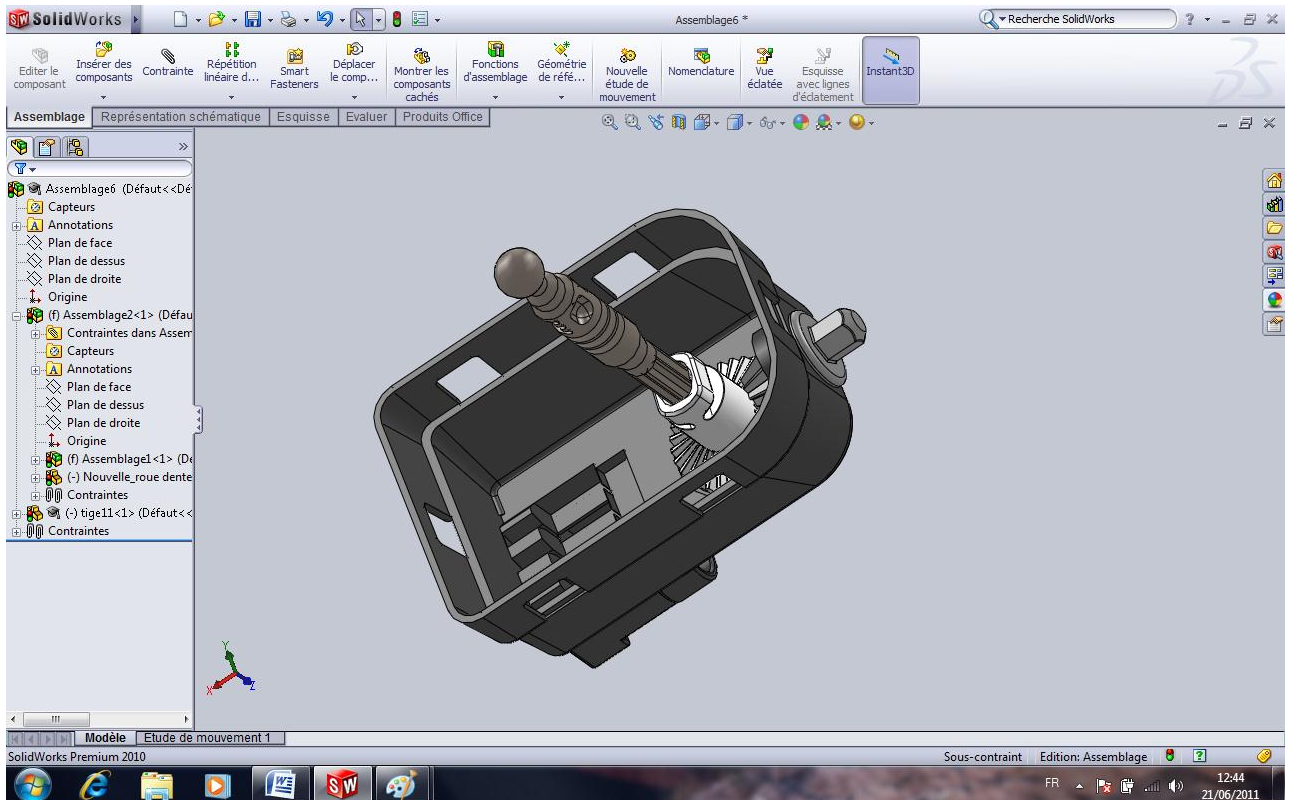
Assemblage 3(assemblage 2+axe de sortie)
